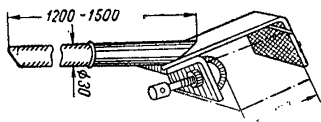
Приспособление для очистки и шлифовки поверхностей
